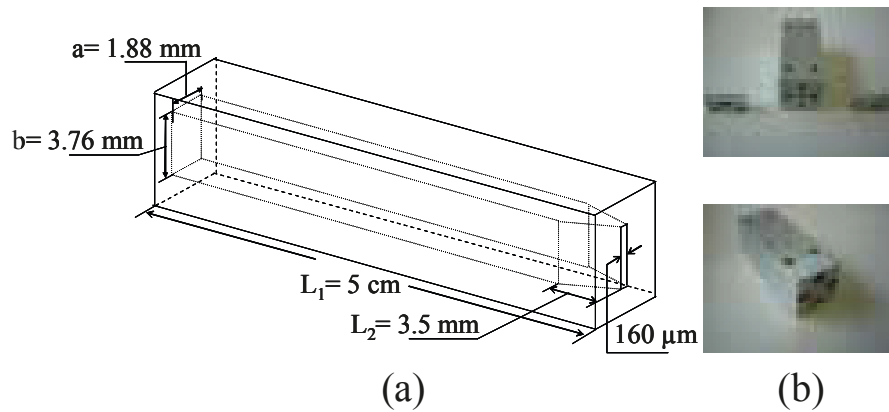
(a) Dimension du guide à fente. (b) Photographie de la sonde à fente micro-usinée avant et après assemblage. [27]
